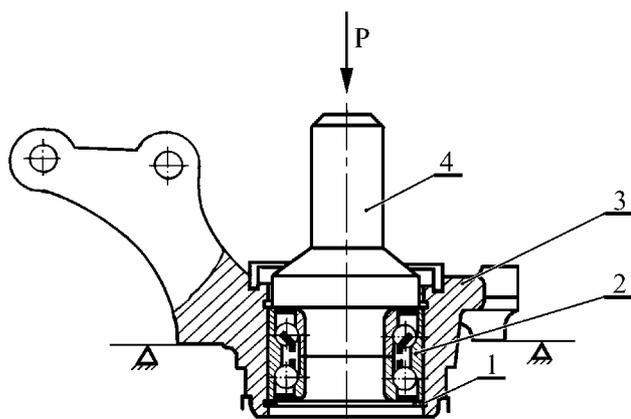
Выпрессовка из кулака и запрессовка в кулак подшипника ступицы переднего колеса:
